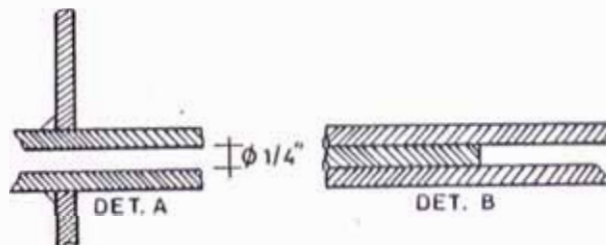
DETALLE DE CONEXION ENTRE PLANCHAS
